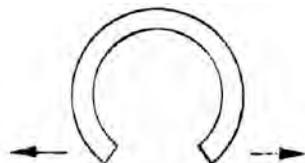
Empaquetadura de la caja de empaquetadura: incorrecto
